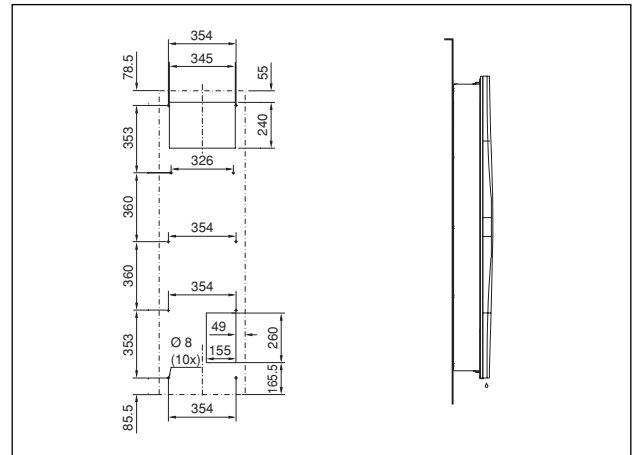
SK 3366.xxx, SK 3377.xxx Påbyggnad
